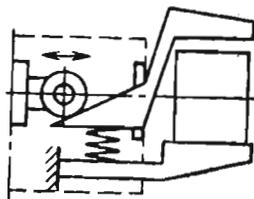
Механическое захватное устройство с неподвижной губкой
